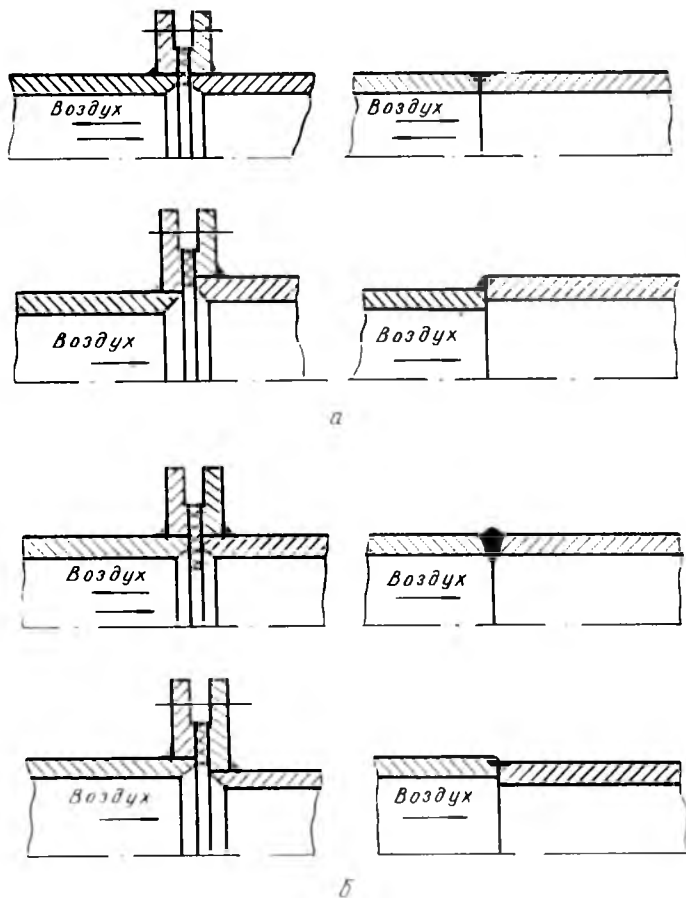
Схемы фланцевого и сварного соединения трубопроводов:
